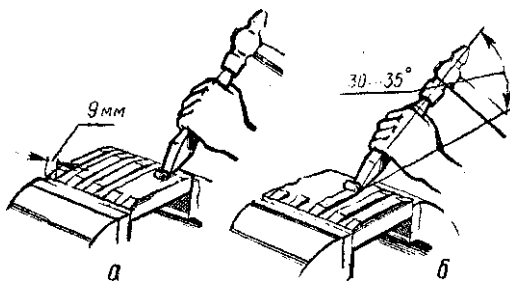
Рубання широких поверхонь: а — прорубування канавок крейцмейселем; б — зрубання виступів зубилом
